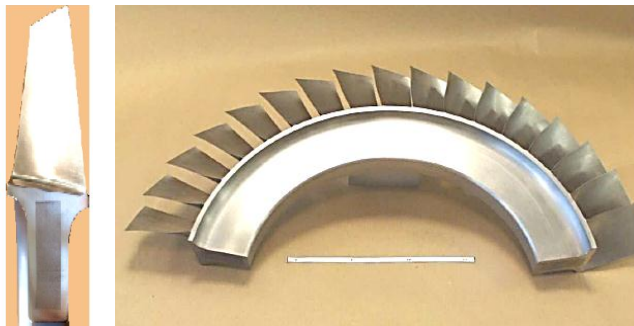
Металлический композиционный материал на основе титана, армированного непрерывными волокнами SiC, и сегмент диска компрессора конструкции типа «блинг»
